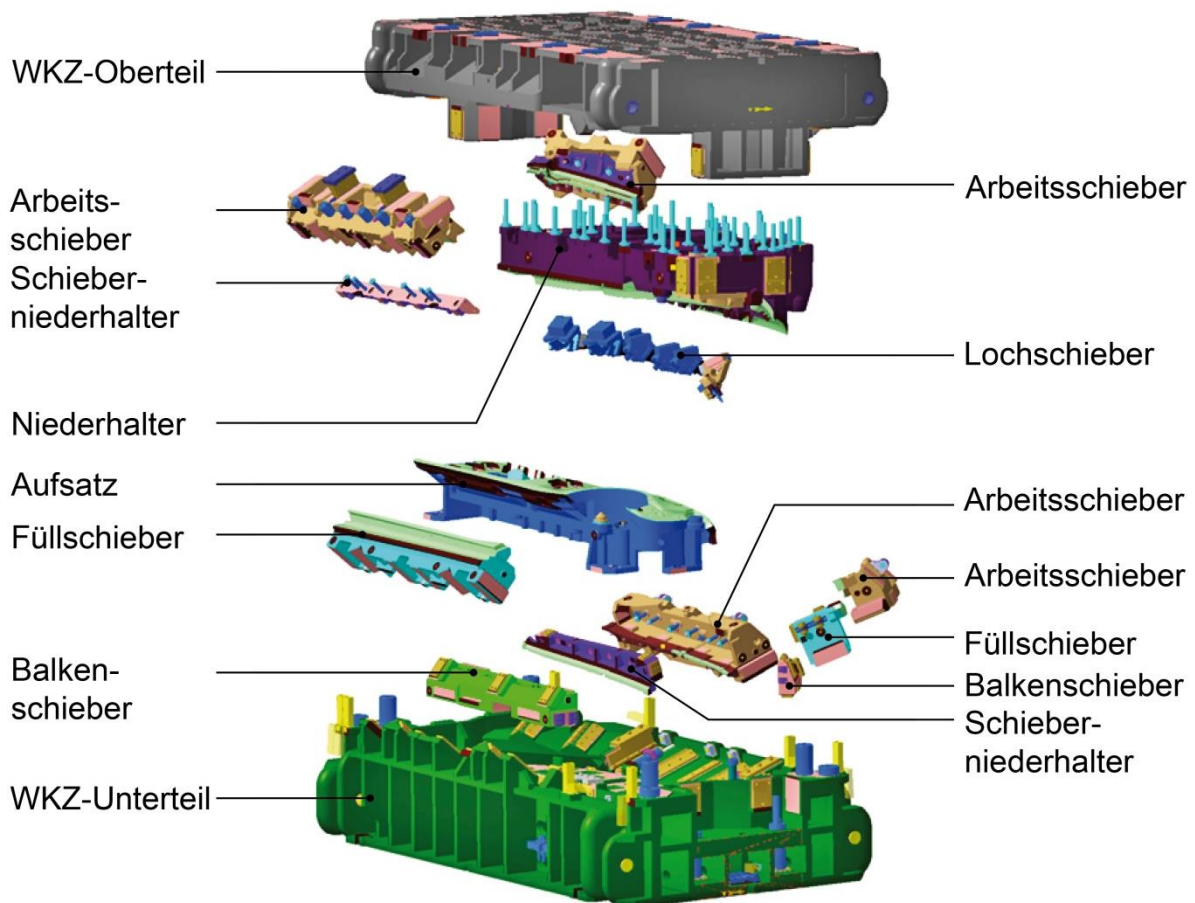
Explosionszeichnung Seitenwandrahmen Werkzeug AUDI A3 Sportback OP50
